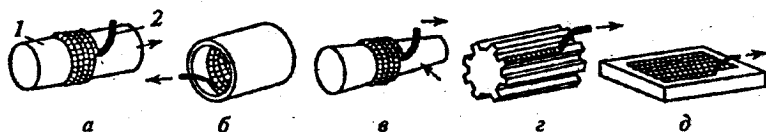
Схемы вибродуговой наплавки изношенных поверхностей:
